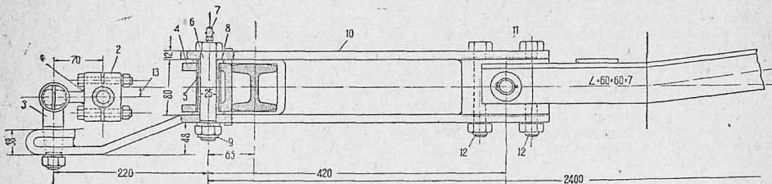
Схема прицепного приспособления для буксировки автомобилей: 1 — блокирующая муфта; 2 — крышка блокирующей муфты; 3 — поворотный кулачок; 4 — башмак, крепящийся к передней оси автомобиля; 5 — внешняя втулка поворотного шкворня; 6 — поворотный шкворень; 7 — масленка; 8 — внутренняя втулка поворотного шкворня; 9 — гайка, крепящая шкворень; 10 — тяга; 11 — поворотный шкворень тяг; 12 — болты $\frac{5}{8}$ " длиной 125 мм, крепящие тягу; 13 — пробка, блокирующая муфту
